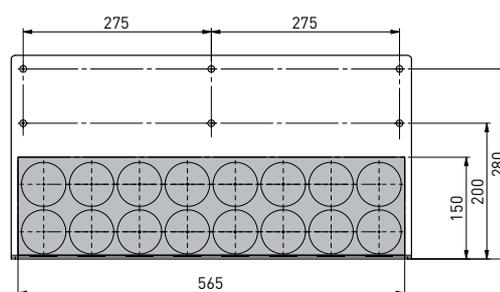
Praticare dei fori di montaggio per il passante tubo nella stiva di stoccaggio
